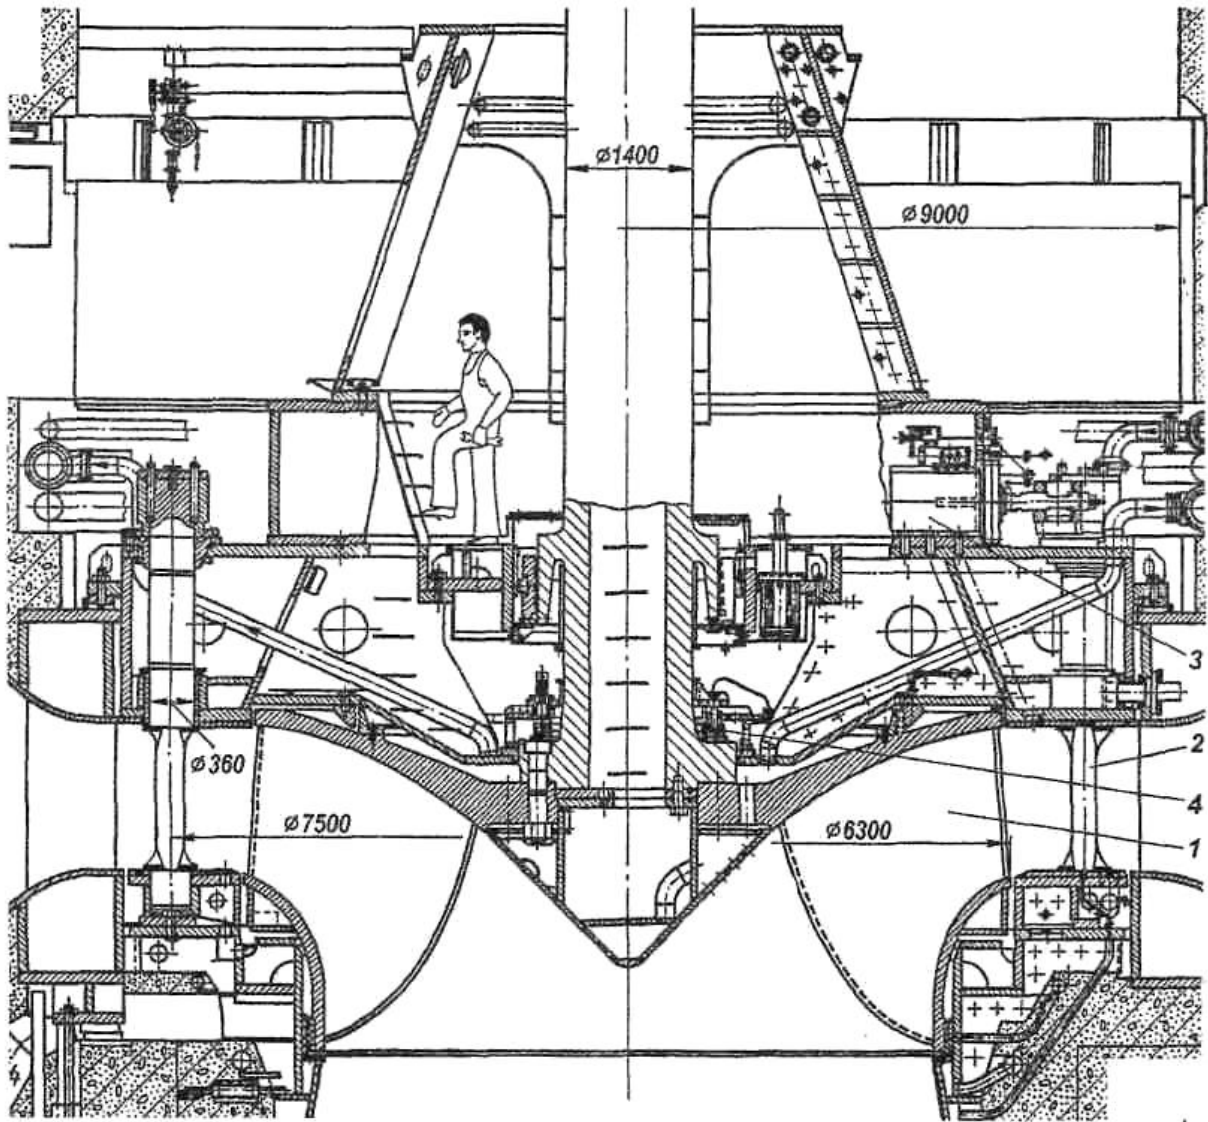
Двомашинний оборотний гідроагрегат типу РОНТ-115:
